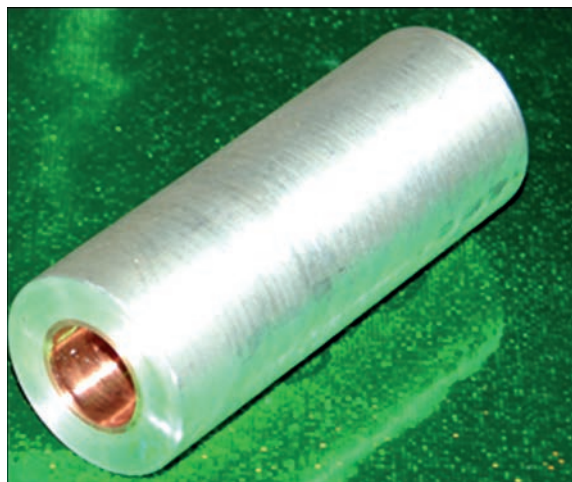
Зразок біметалічної трубної заготовки (АД1 – зовнішній шар, М2 – внутрішній)
